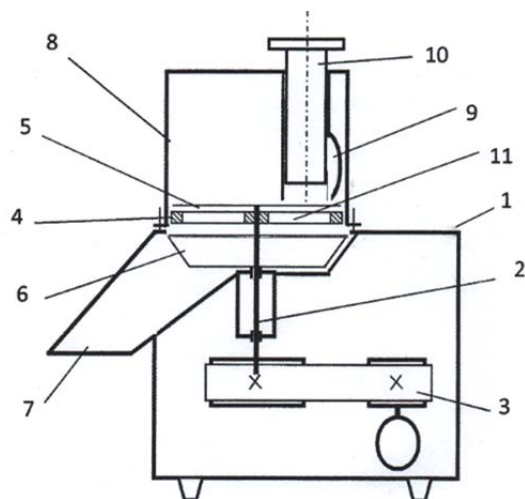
Кинематическая схема: 1 — корпус; 2 — вертикальный приводной вал; 3 — привод, состоящий из электродвигателя и клиноременной передачи; 4 — опорные диски; 5 — ножи; 6 — сбрасыватель; 7 — разгрузочное отверстие; 8 — загрузочное устройство; 9 — рабочая камера; 10 — толкатель; 11 — отверстия опорных или тёрочных дисков
